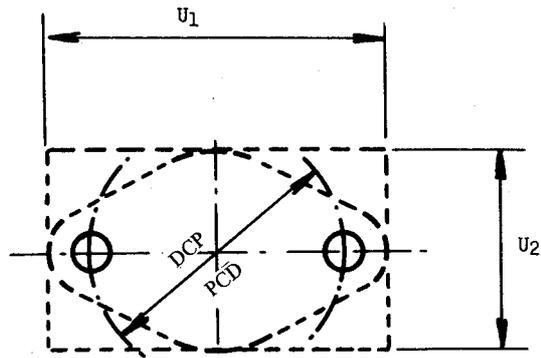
Encombremens d'embase plates en forme de losange ou de rectangle.
